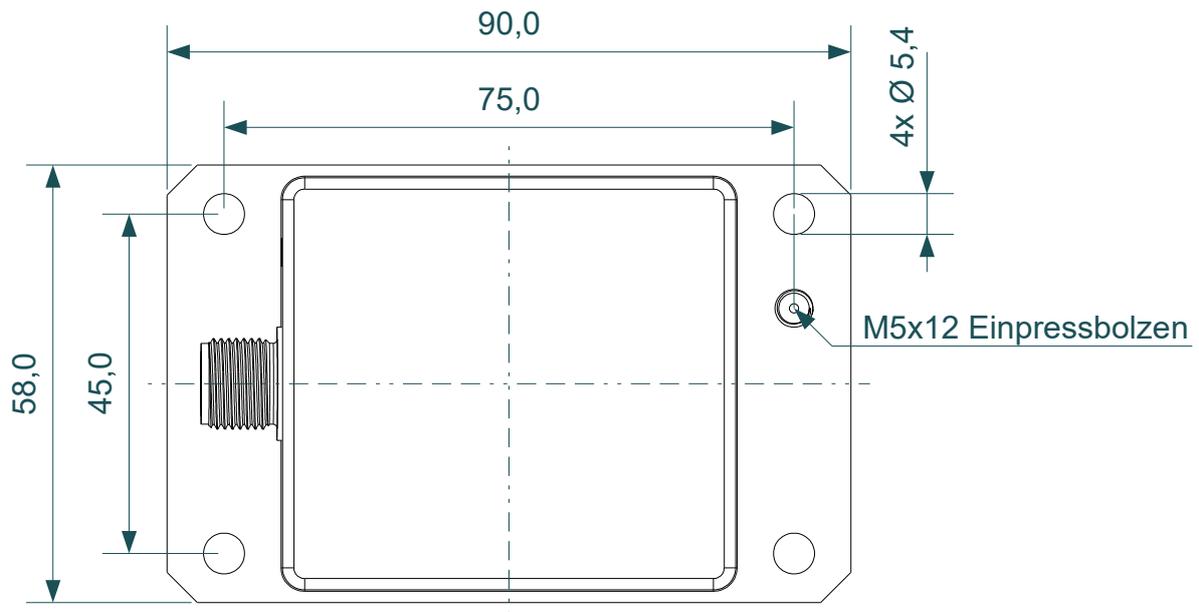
Befestigungsbohrungen Aluminiumgehäuse (MA) (Maße in mm)
